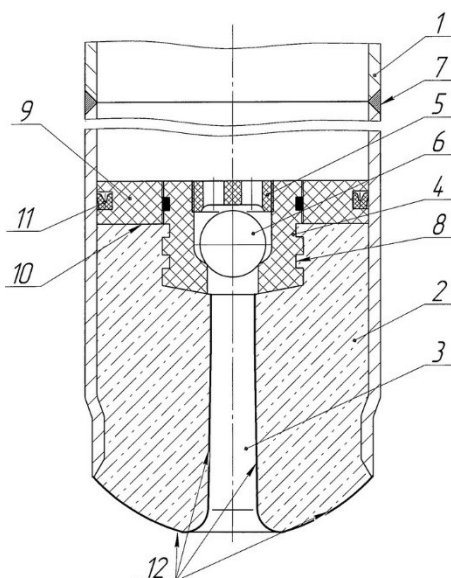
Разбуриваемый башмак-клапан для установки расширяемой колонны в скважине на котором 1 – металлический патрубок, 2 – корпус, 3 – центральный проходной канал, 4 – полая цилиндрическая вставка, 5 – негерметичная заглушка, 6 – шаровой клапан, 7 – сварка, 8 – кольцевые проточки, 9 – цилиндрическая площадка, 10 – герметизирующее пространство, 11 – манжета, 12 – наружная поверхность.
